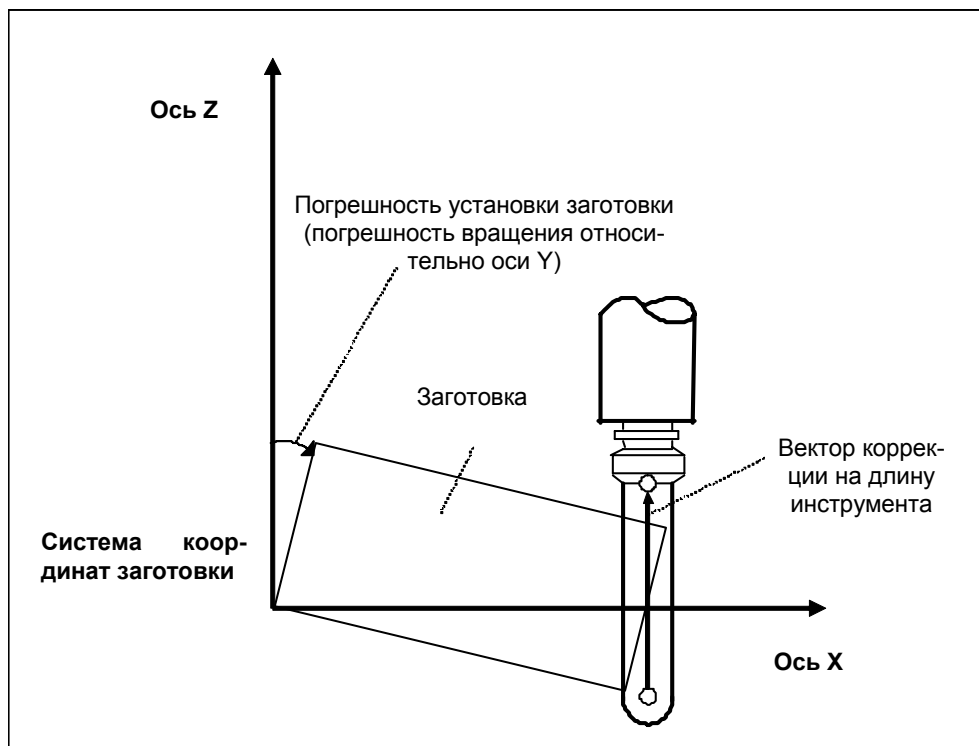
(s) Заготовка обрабатывается боковой стороной инструмента при наличии погрешности на установку заготовки (Если RCM=0)
